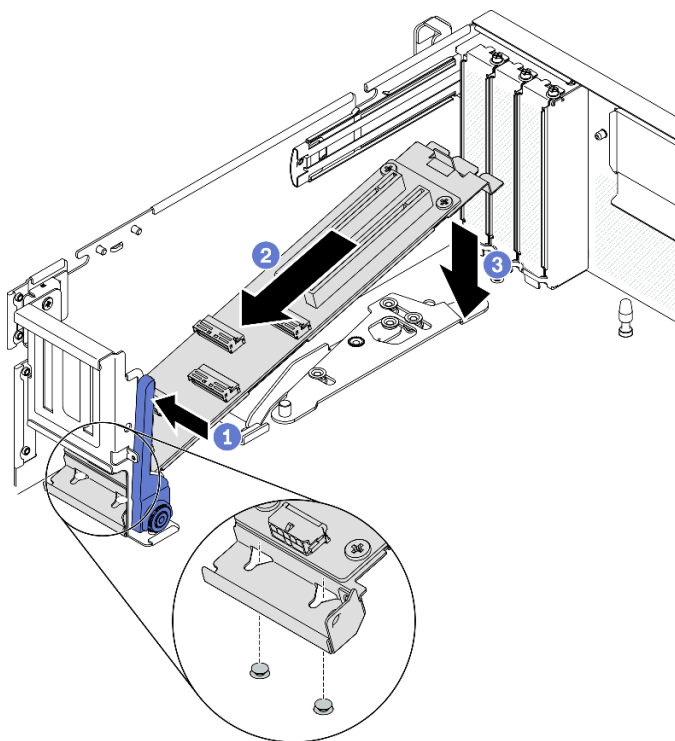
Colocando o módulo de placa de expansão de E/S frontal no chassis
